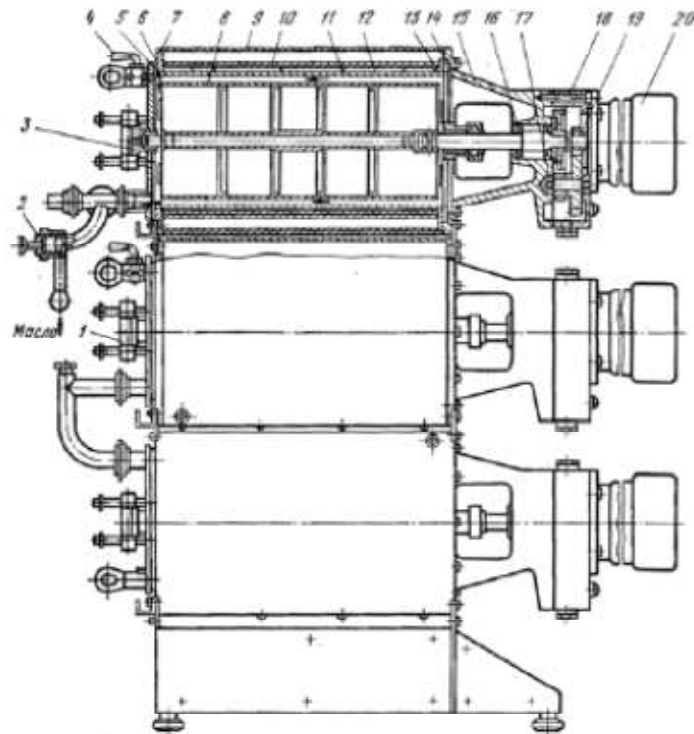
Маслоутворювач Т1-ОМ-2Т: 1-кронштейн; 2-кран випускний; 3-втулка напрямляюча; 4-кран повітряний; 5-кришка; 6-кільце ущільнювальне; 7-фланець циліндра передній; 8-витіснювальний барабан; 9-обшивка циліндра; 10-обечайка циліндра зовнішня; 11-спіраль; 12-обечайка циліндра внутрішня; 13-фланець циліндра задній; 14-кільце ущільнювальне; 15-редуктор; 16,17-підшипники; 18,19-шестерні; 20-електродвигун; 21-ножі; 22-станина.
